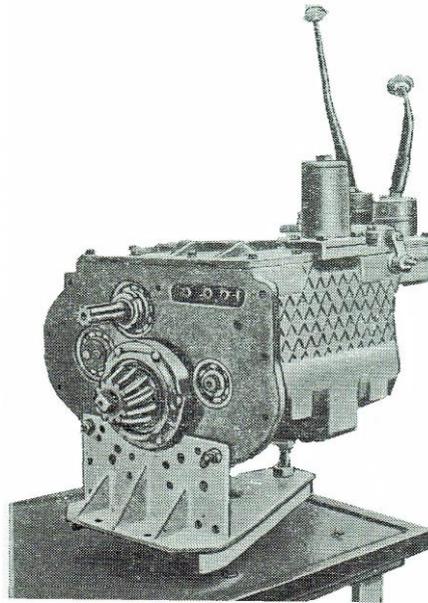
Схема станда ОПр-626 для разборки и сборки коробок передач.
